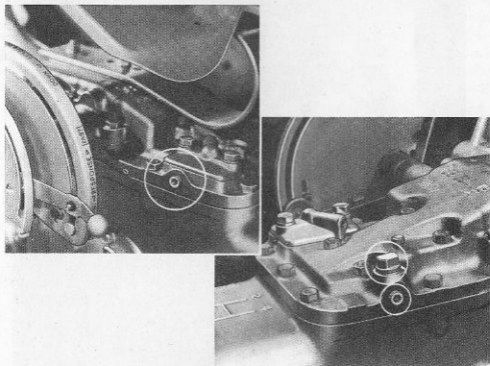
Tryckoljeuttag på hydrauliska systemets lock
